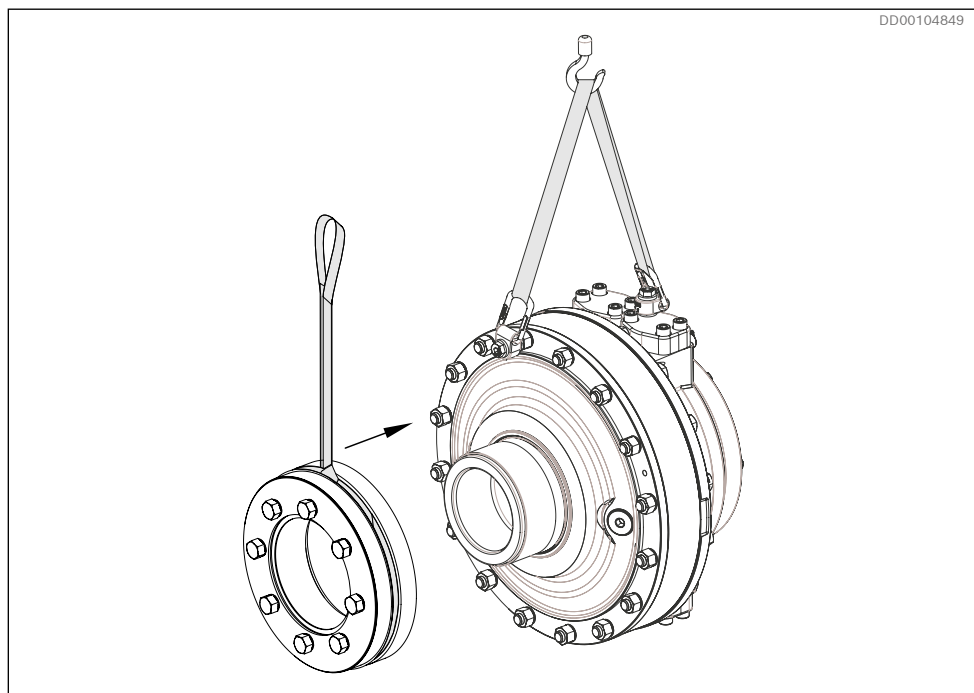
Instalación del disco compresor en el motor de acoplamiento
